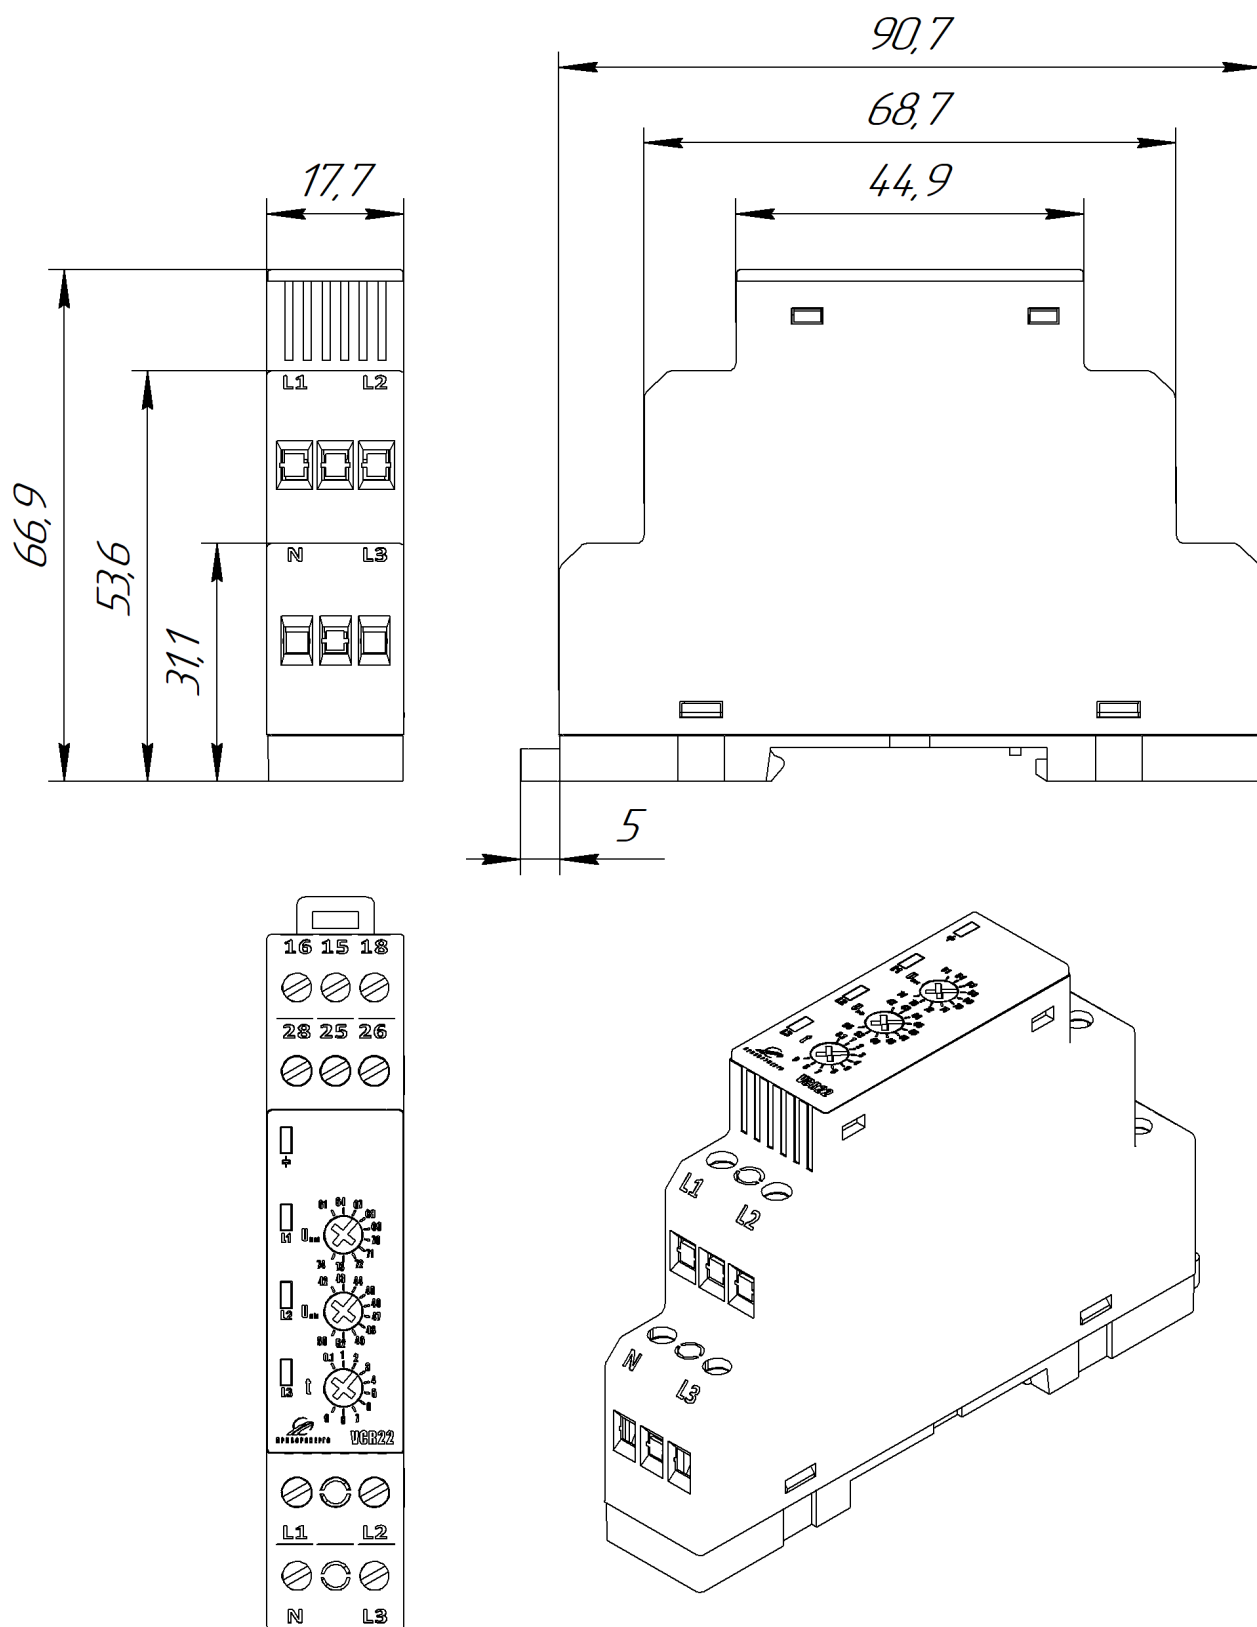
Габаритные размеры реле контроля напряжения VCR22
